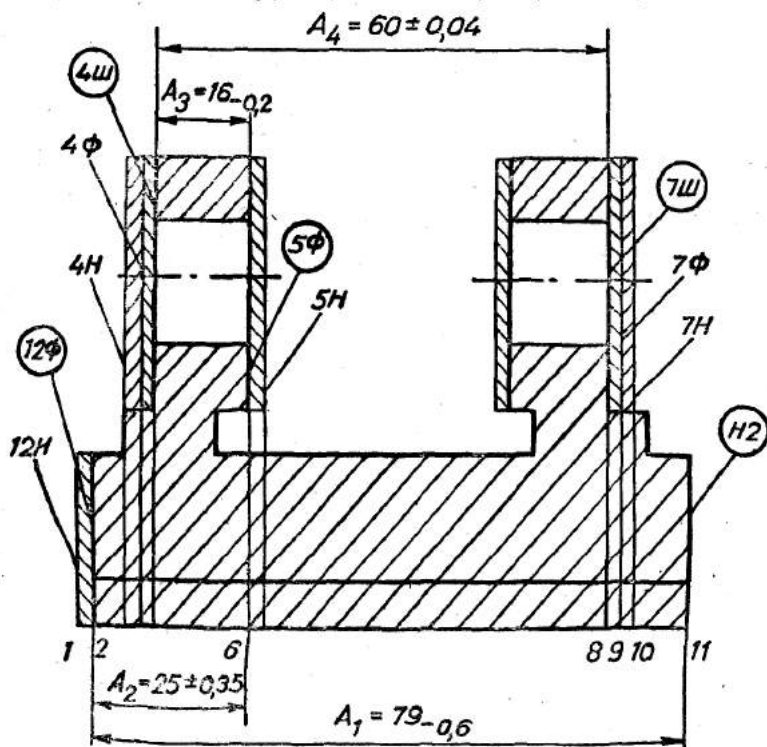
Розмірна схема зв'язків необроблених (Н), фрезерованих (Ф) та шліфованих (Ш) поверхонь опори поворотної.
